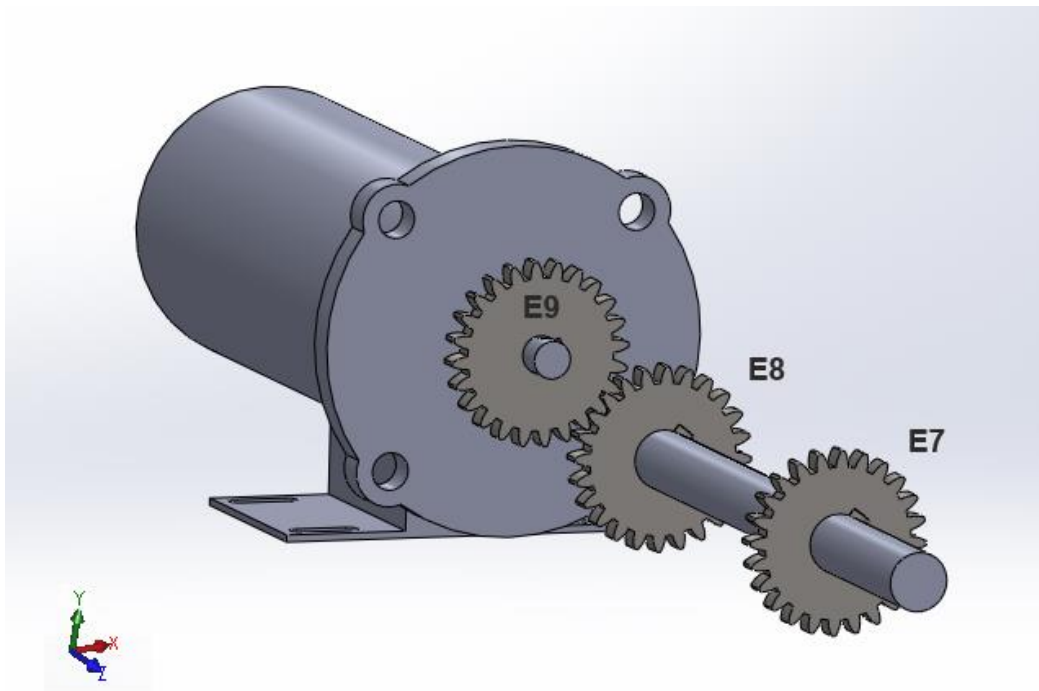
Vista isométrica del engranaje 7, engranaje 8 y engranaje 9. Fuente: Elaboración propia.
